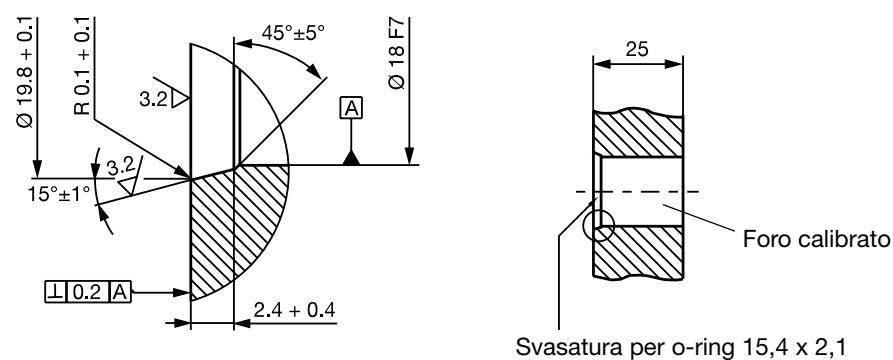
Foro calibrato per il montaggio del BTL con o-ring
